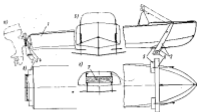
Схема крыльцового устройства и монтажных частей дюралевой лодки: а — вид сбоку; б — вид на носовое крыло; в — вид на днище; д — вид на корму.
